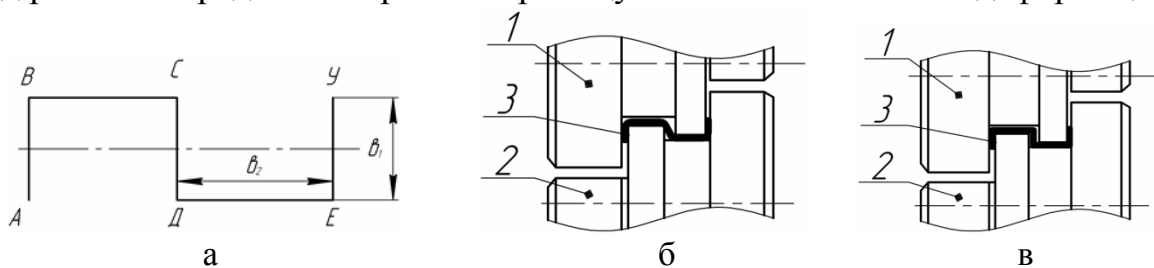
Схема калибровки валков профилировочного стана: а – сечение профиля металлорукава; б – калибр в клетке 1; в – калибр в клетке 2
